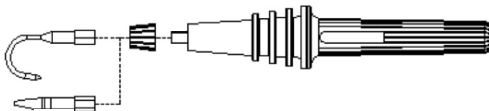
стандартный крючковый и прямой металлические наконечники, внешняя резьба и шестигранное гнездо.
